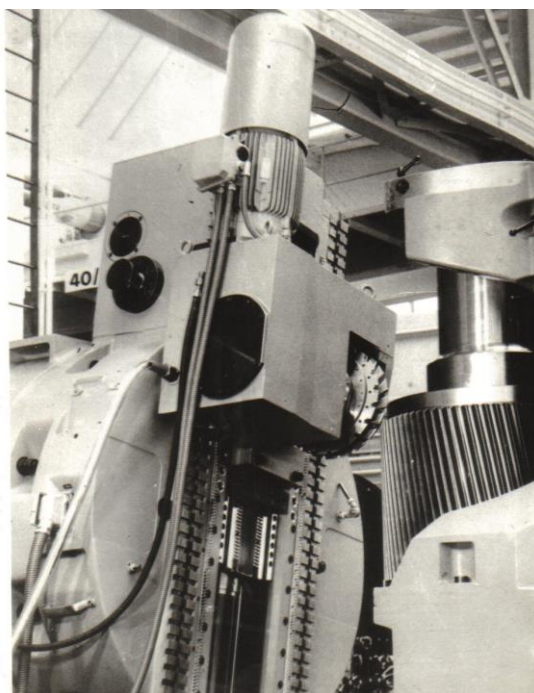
Специальный фрезерный суппорт с дисковыми фрезами
